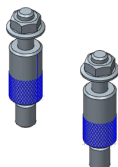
Boulon 3282/45 (1 jeu = 2 pièces)
